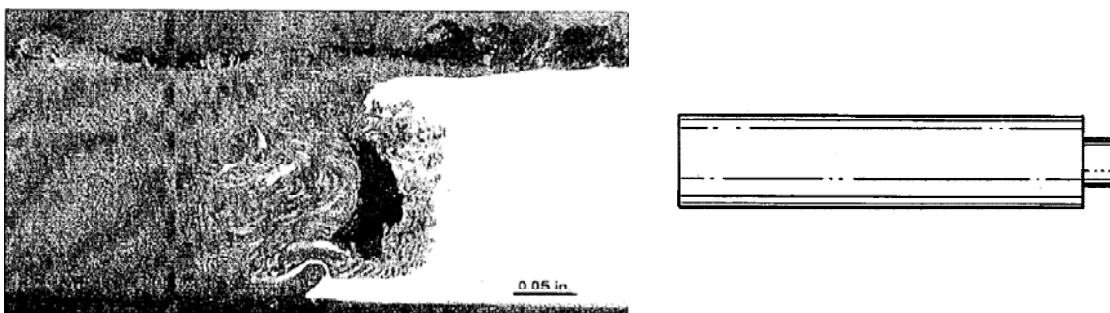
Erste Schweißversuche mit einem konventionellem Alu-FSW-Werkzeug (rechts) an zwei verschiedenfarbigen ABS-Platten (links) [1 S. Fig.1&2]
